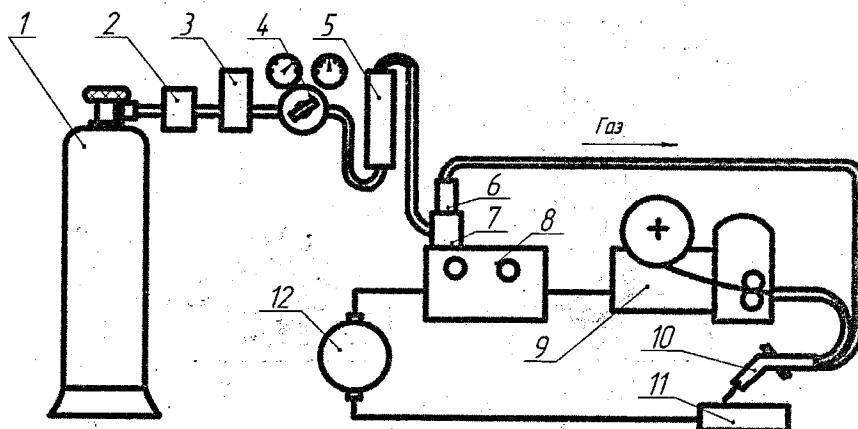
Схема установки для напівавтоматичного зварювання або наплавлення в середовищі вуглекислого газу:
